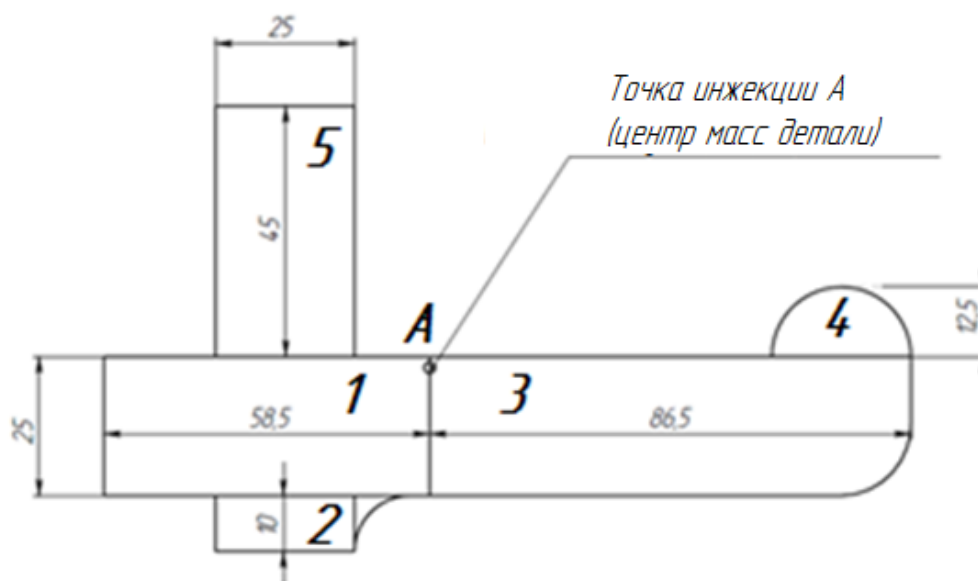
Схема формообразующих поверхностей пресс-формы
